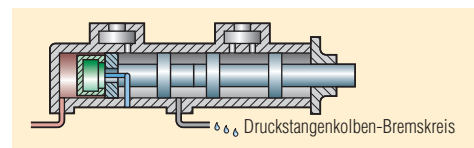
Tandem-Hauptzylinder mit defektem Druckstangenkolben-Bremskreis.
